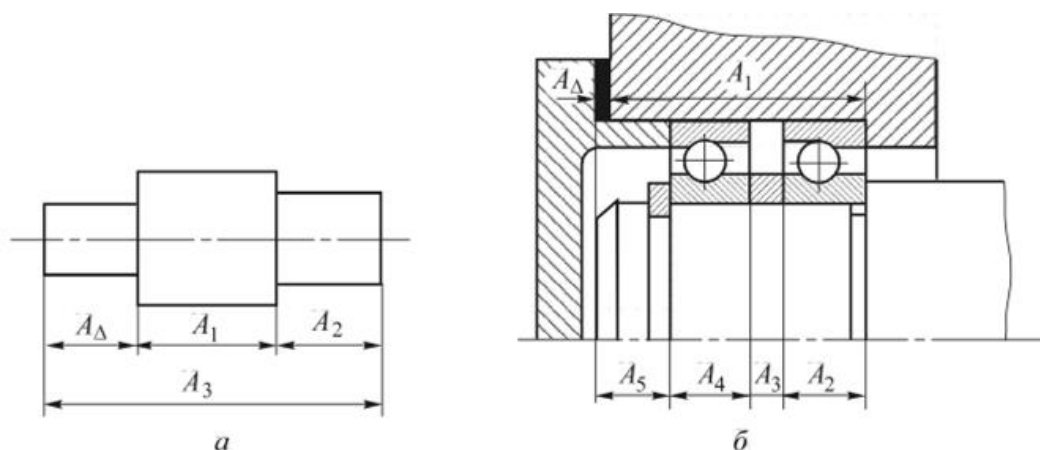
Примеры образования размерных цепей: подетальной (а) и сборочной (б)
